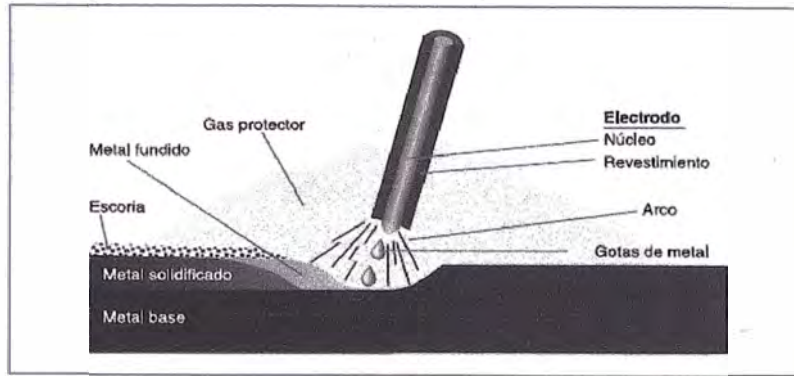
Esquema Proceso SMAW (Fuente: Manual de Soldadura Indura)
